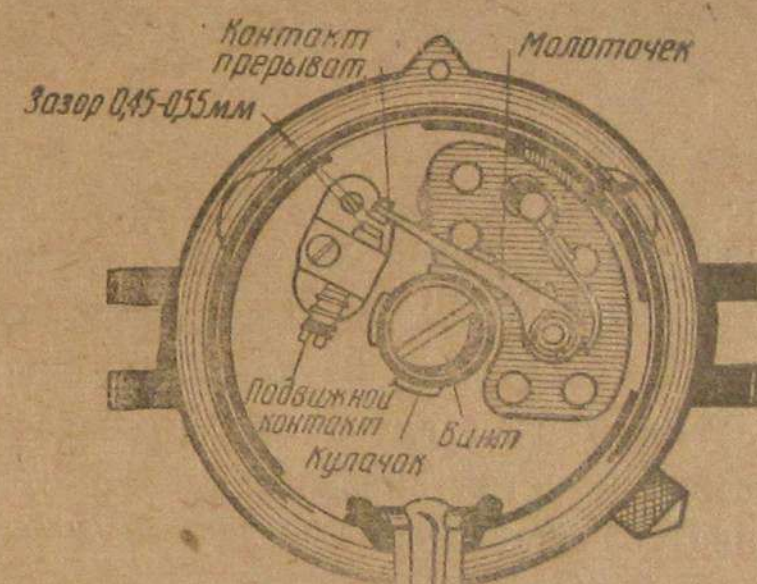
Прерыватель двигателя ГАЗ (схема)
